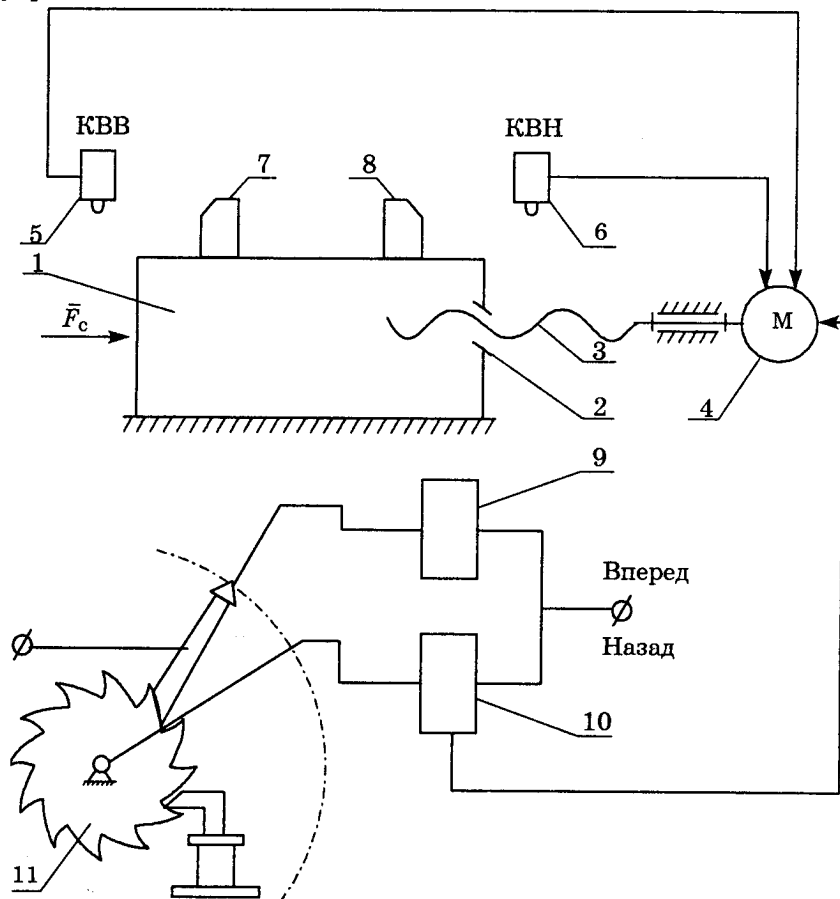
Управление и перемещение с помощью конечных выключателей и шагового искателя: 1 — рабочий орган; 2 — гайка; 3 — винт; 4 — двигатель; 5, 6 — конечные выключатели КВВ (вперед) и КВН (назад); 7, 8 — упоры; 9, 10 — реле "вперед" и "назад"; 11 — шаговый искатель
